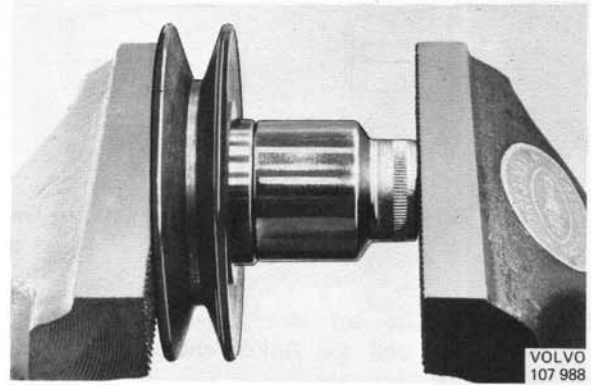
Einpressen des Kugellagers in die Spannrolle, früh. Ausf.
